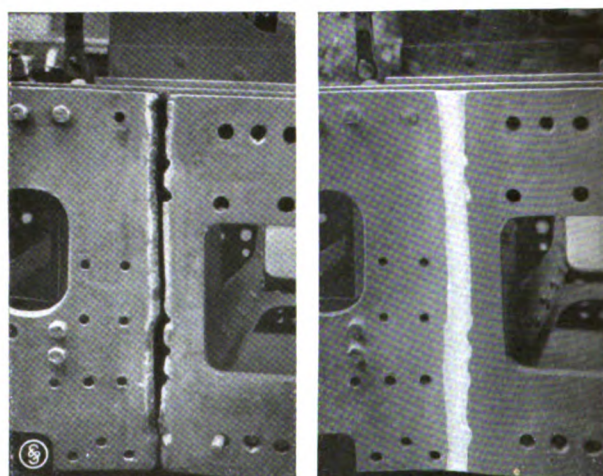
Schweißung eines gebrochenen Lokomotivrahmens. Links: vor der Schweißung. Rechts: nach der Schweißung.
